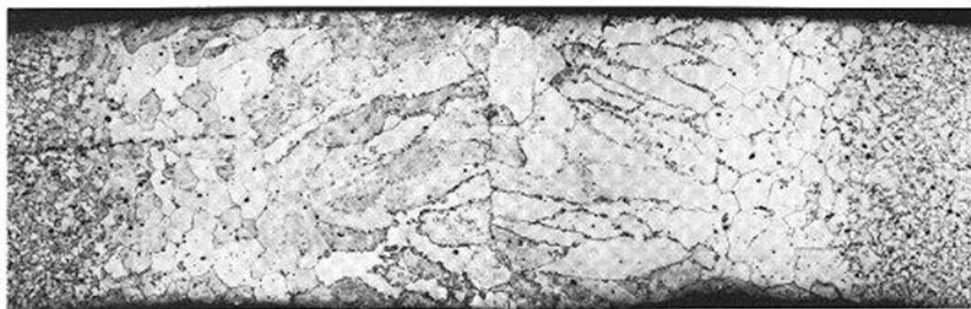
Структура шва и околошовной зоны при аргоно-дуговой сварке
